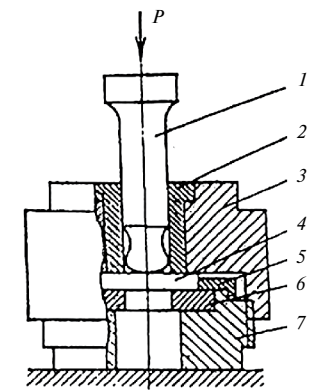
Приспособление для испытания на срез гладкого образца по круговому контуру: 1 – пуансон; 2 – направляющая втулка; 3 – прижимная гайка; 4 – образец; 5 – фиксирующее кольцо; 6 – матрица; 7 – основание.
